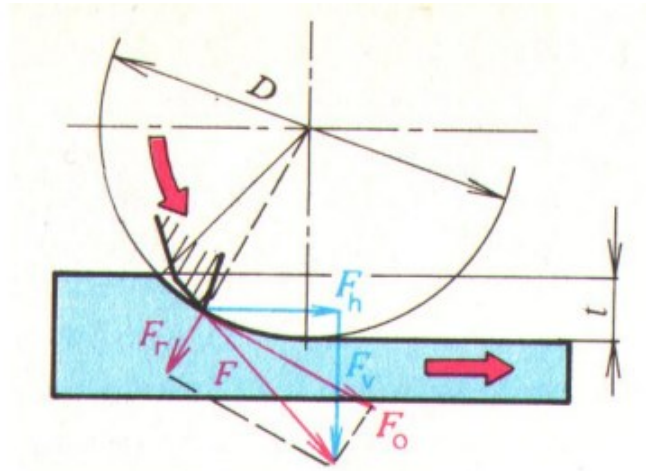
Smysl otáčení při sousledném válcovém frézování.
